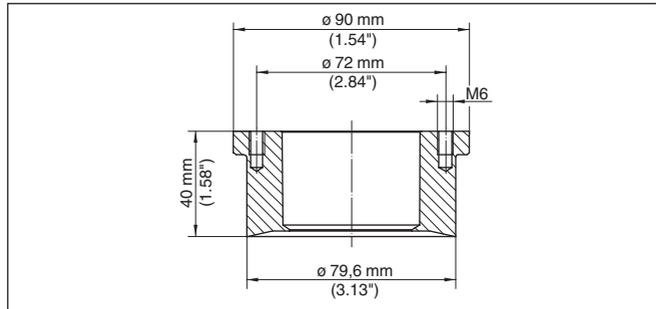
Dimensiones racor para soldar conexión aséptica DN 32 con brida de sujeción
